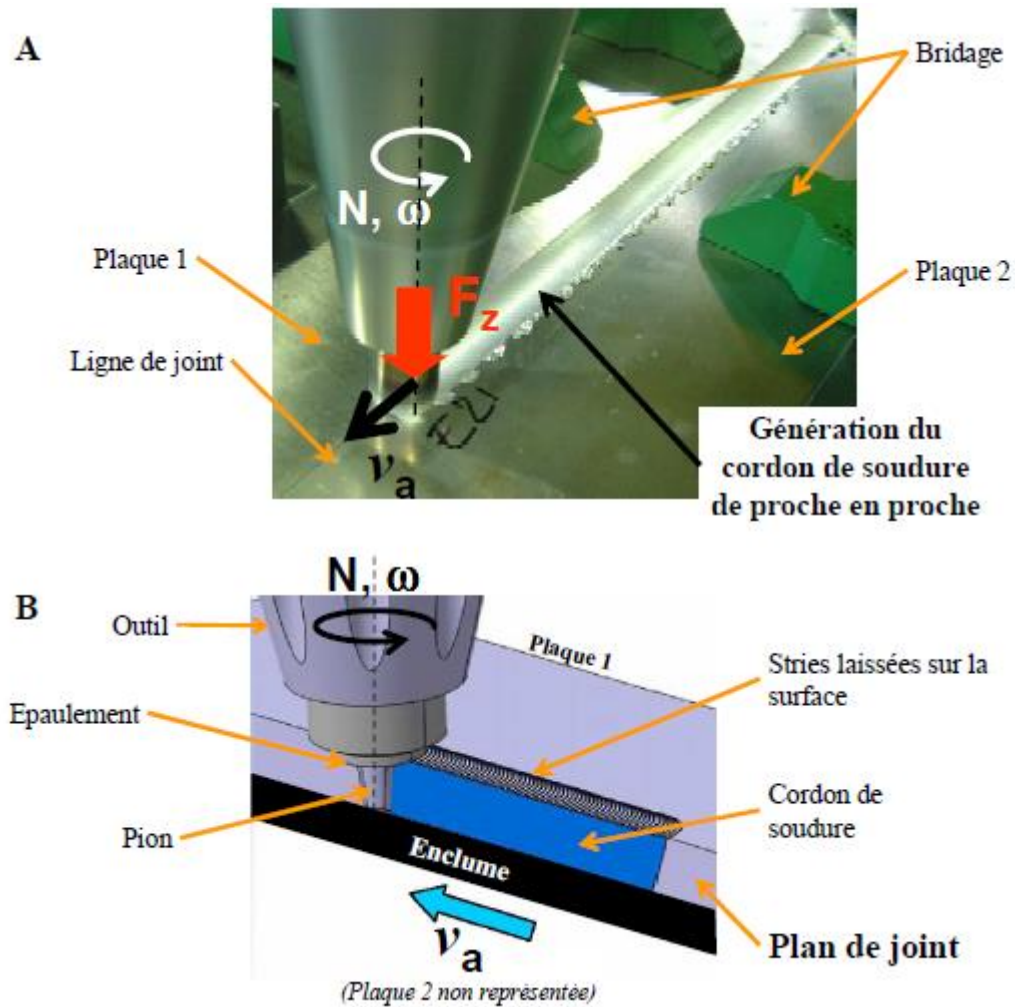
1: Présentation du soudage par friction malaxage. A-Soudure rectiligne de deux plaques mises bout à bout. B-Visualisation du plan de joint lors de la phase de soudure [8].
